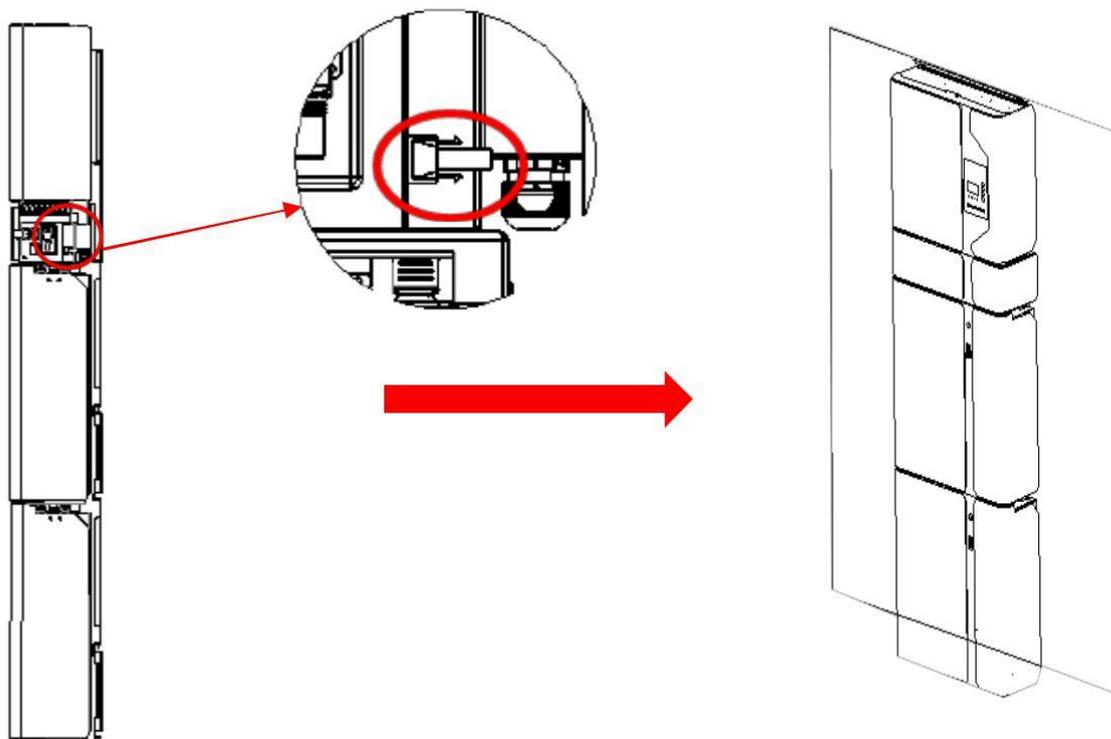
Collegamento delle stringhe impianto fotovoltaico
